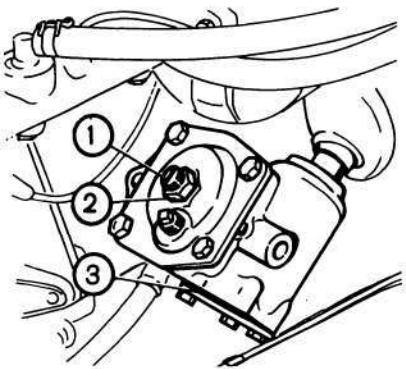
Регулировка зазоров в рулевом механизме: 1 — винт; 2 — гайка; 3 — регулировочные прокладки
